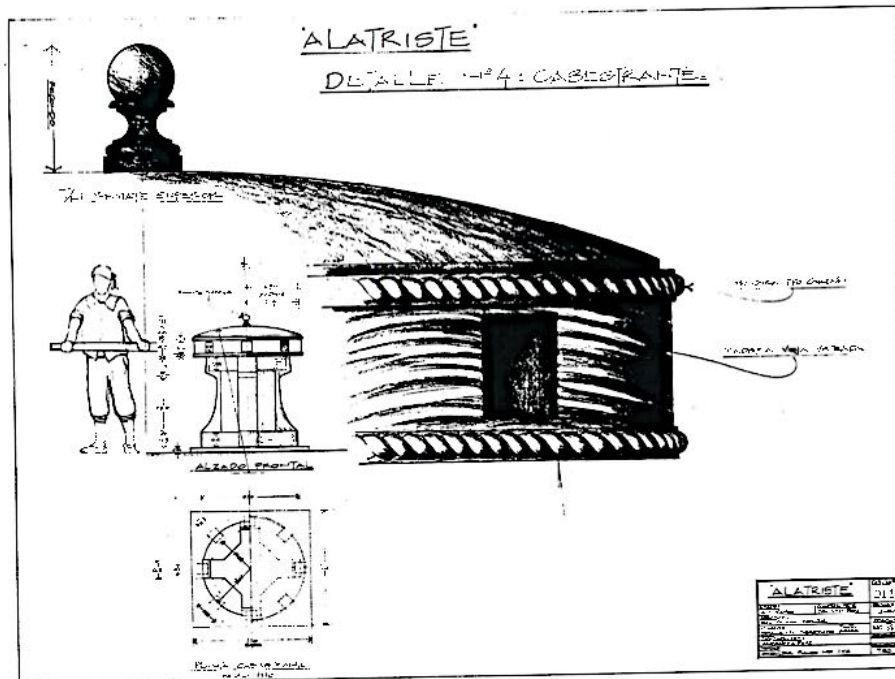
Plano. Galeón. Detalle cabestrante. Alatríste. Fuente: Benjamín Fernández.
